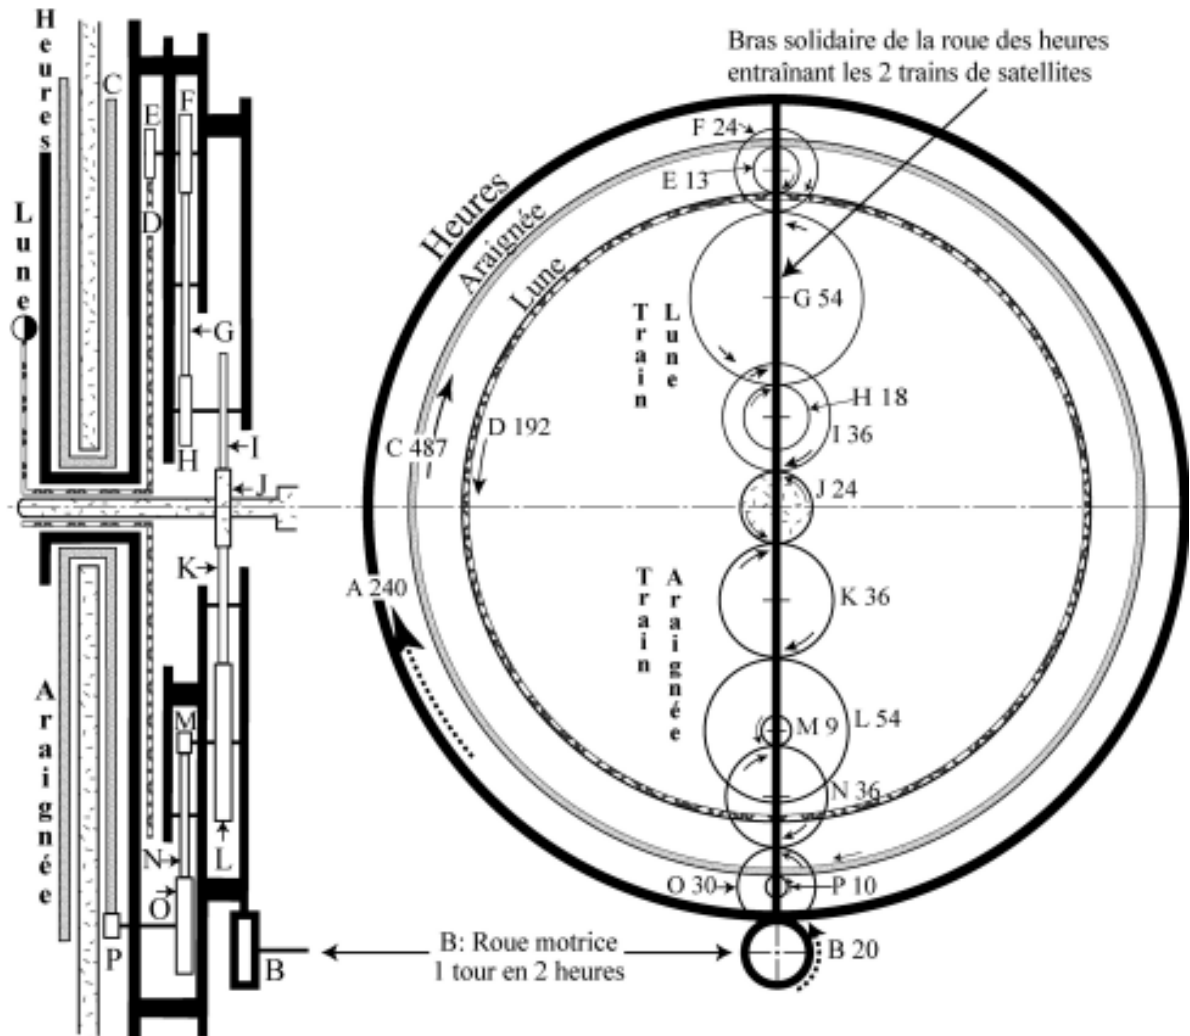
Les engrenages de l’astrolabe (Vue de côté et de face)
